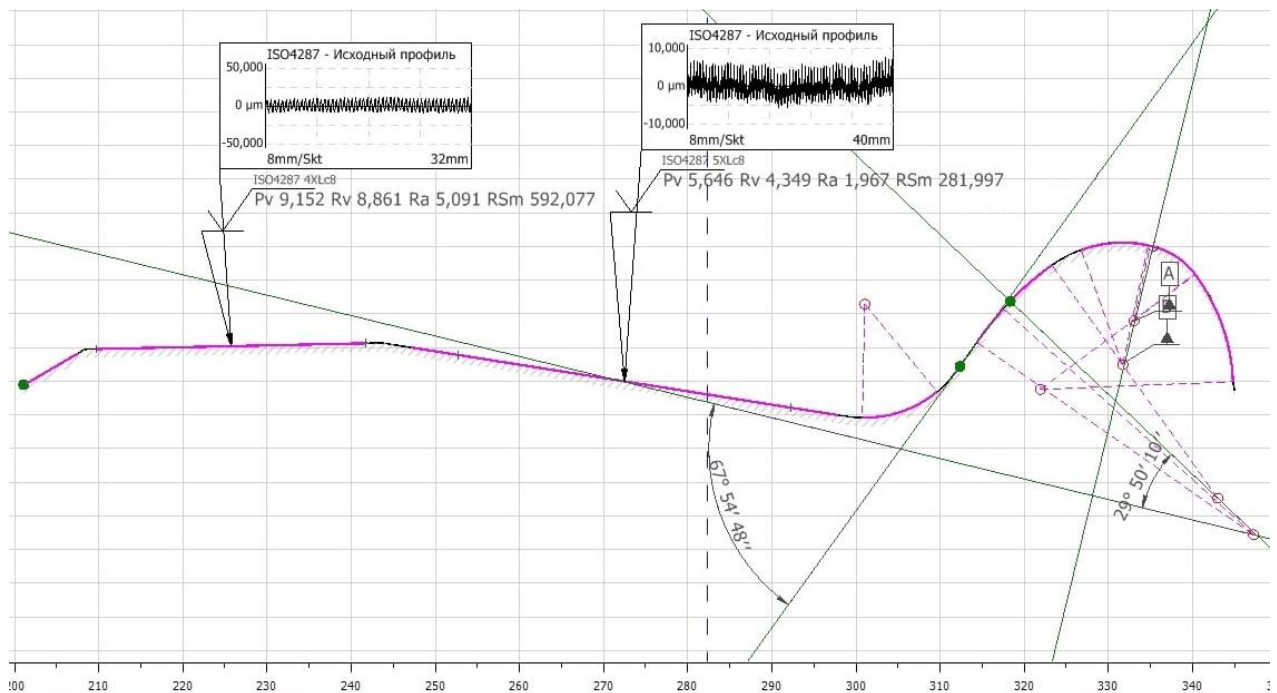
Шероховатость обработанной поверхности катания колесной пары.
